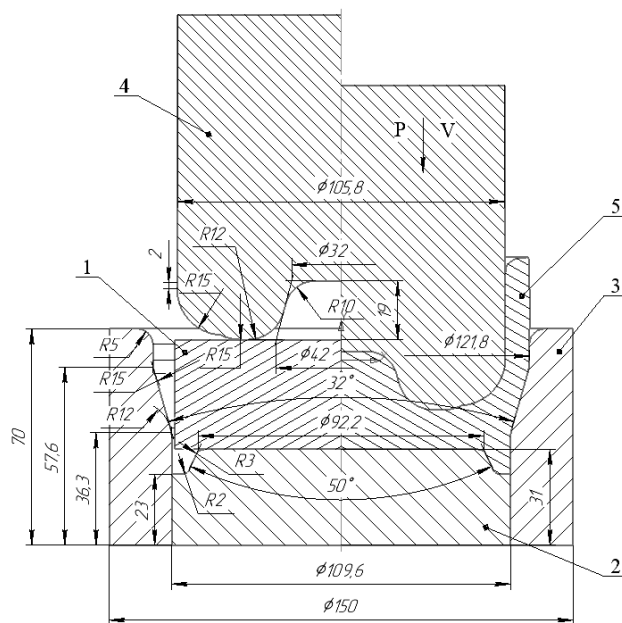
Схема процесу гарячого зворотного видавлювання з роздачою напівфабрикату здеформованого із заготовки круглої форми: 1 – заготовка; 2 – виштовхувач; 3 – матриця; 4 – пуансон; 5 – напівфабрикат
